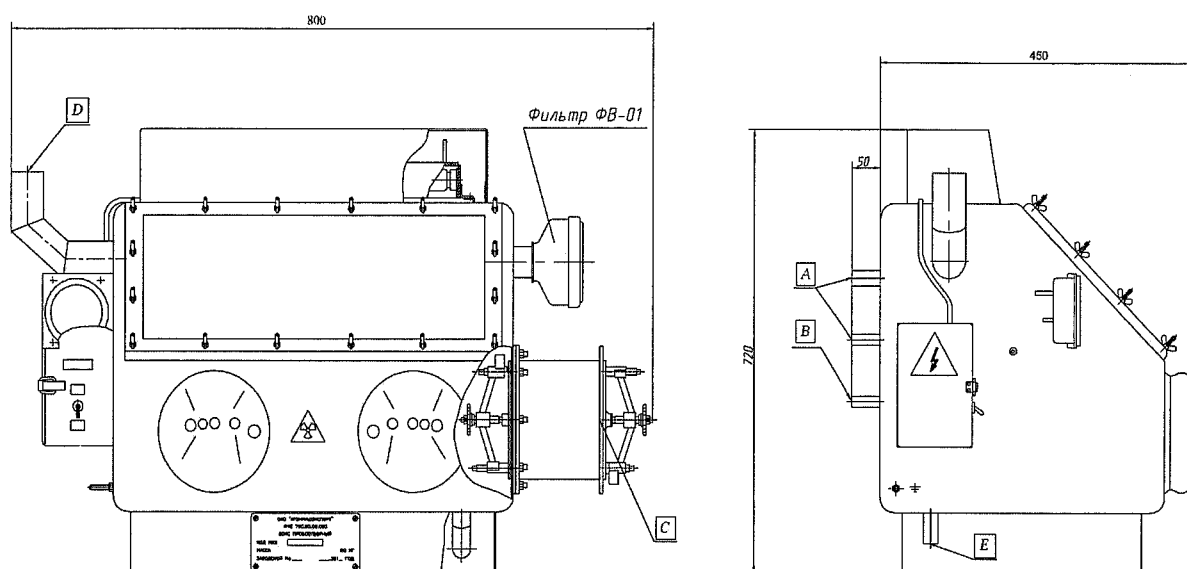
Габаритный чертеж бокса пробоотборного
